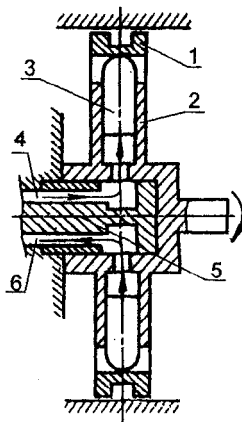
Роторно-поршневой насос (вид сбоку):
